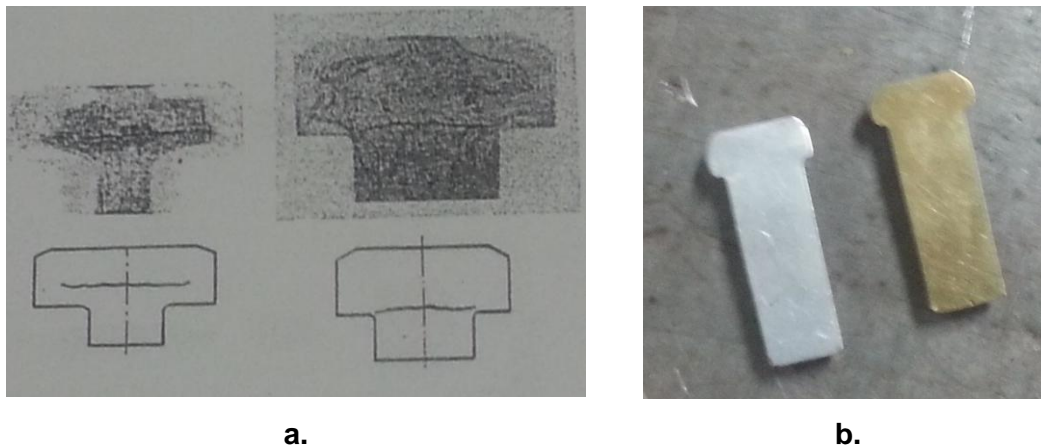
Grietas internas. a) Posición de grietas internas⁵³. b) Piezas recalçadas cortadas a la mitad⁴⁸
